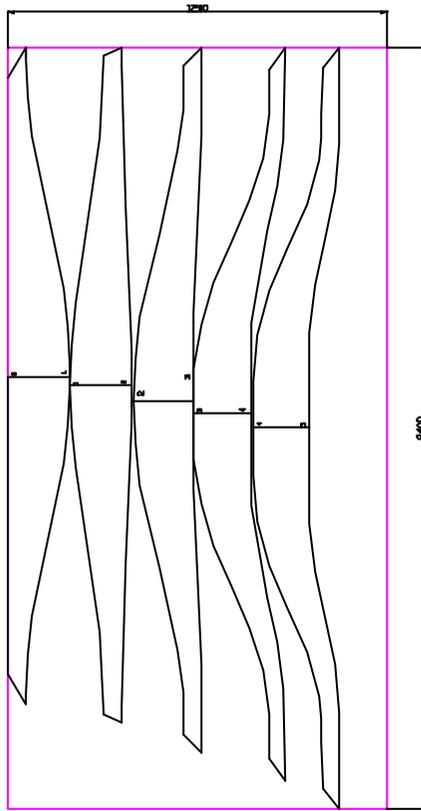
Ubicación de las plantillas del tubo de succión en la plancha de acero para el trazado y oxicorte (Segmentos 1-1 al 4-5)
